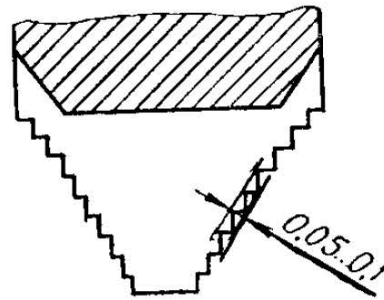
Прорізний зуб дискової чорнкової модульної фрези
